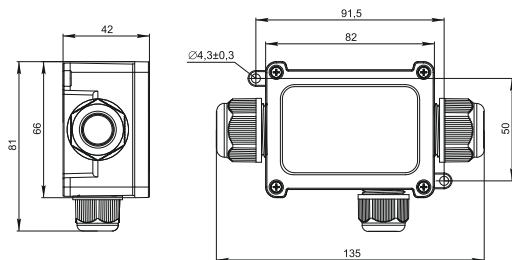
Габаритные размеры коробки WTP-411 / Figure 11 – Overall dimensions of the WTP-411 box
